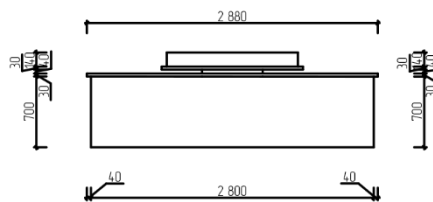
Чертёж фонтана. Вид сбоку
